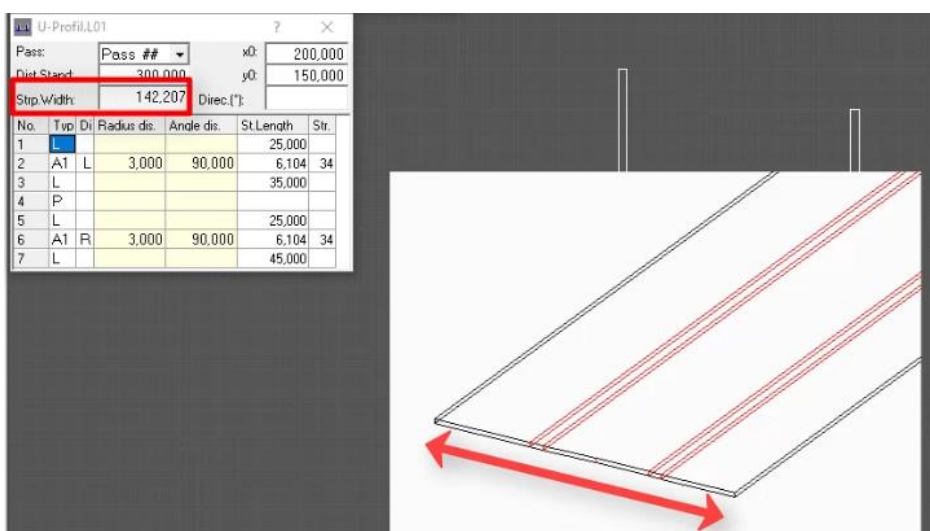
Розрахована автоматизовано довжина ширини заготовки для виготовлення профілю
